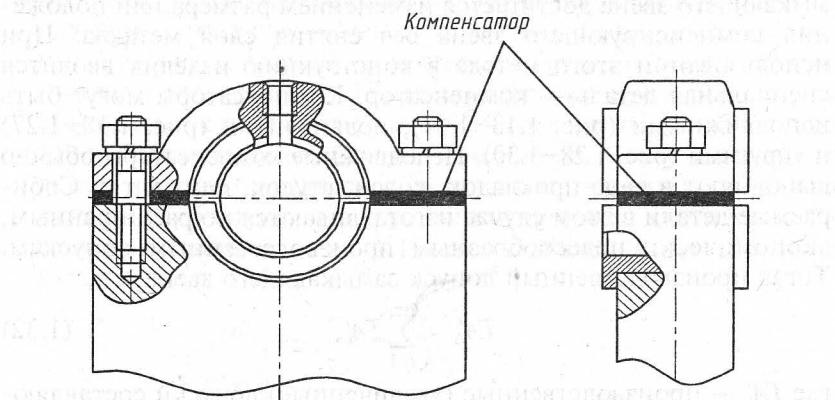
Способ регулировки радиального зазора в подшипнике скольжения
